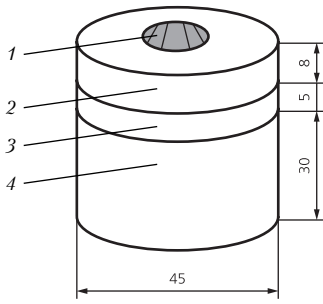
Схема цилиндрического наплавленного образца для расчета:
